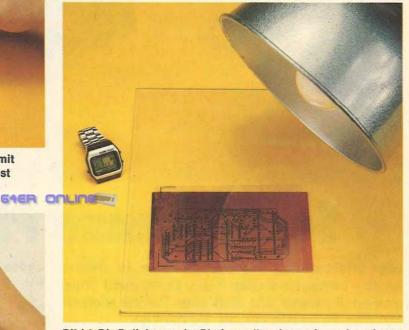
Die Belichtung der Platine sollte eher zu kurz als zu lange sein. Die Fassung der Birne muß die Leistung verkraften.
